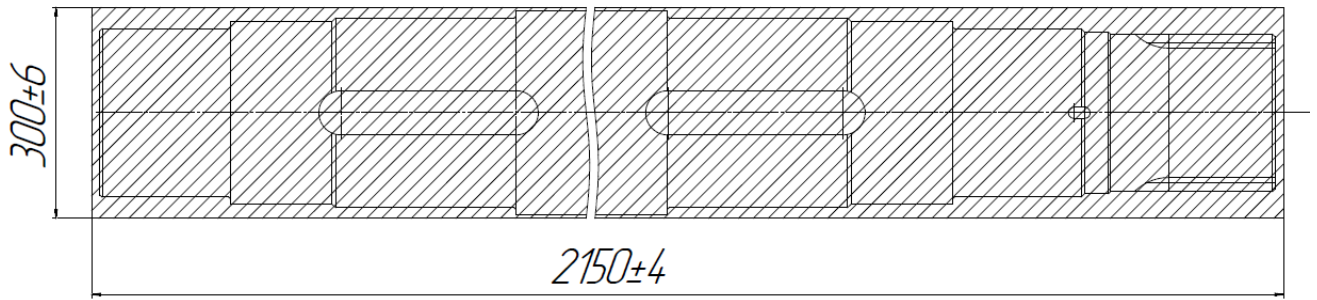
Ескіз заготовки деталі «Вал»
